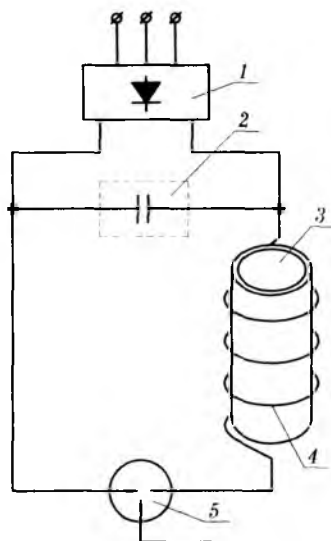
Схема установки для магнитной импульсной формовки:
